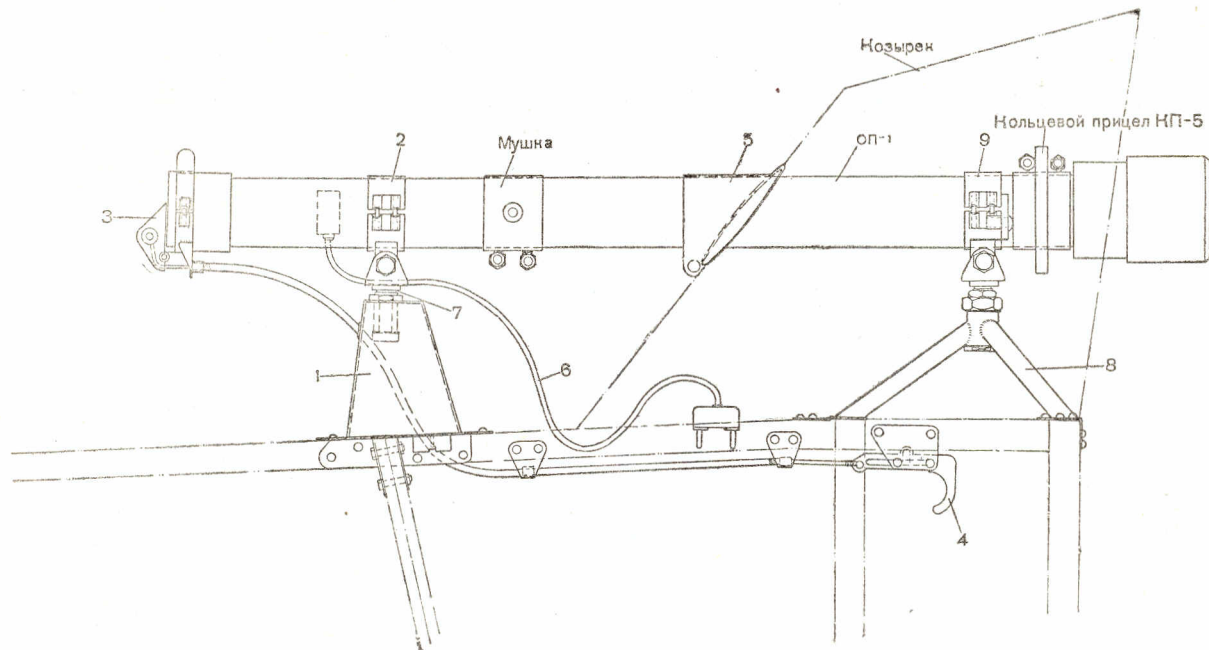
Схема установки ОП-1 (1-й вариант, вид сбоку).
